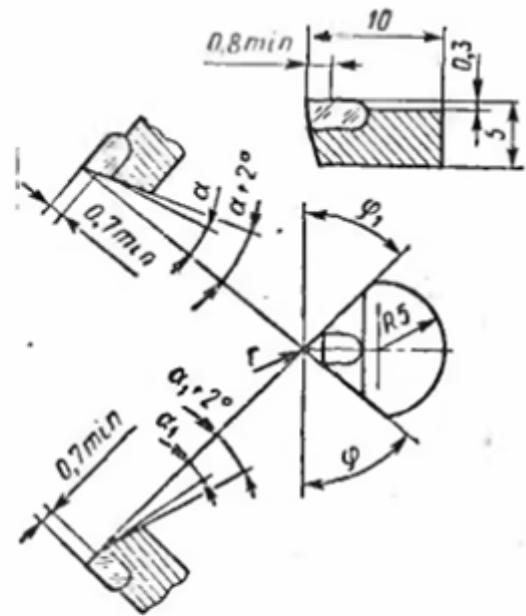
Конструкция и размеры металлокерамической вставки с режущим элементом
